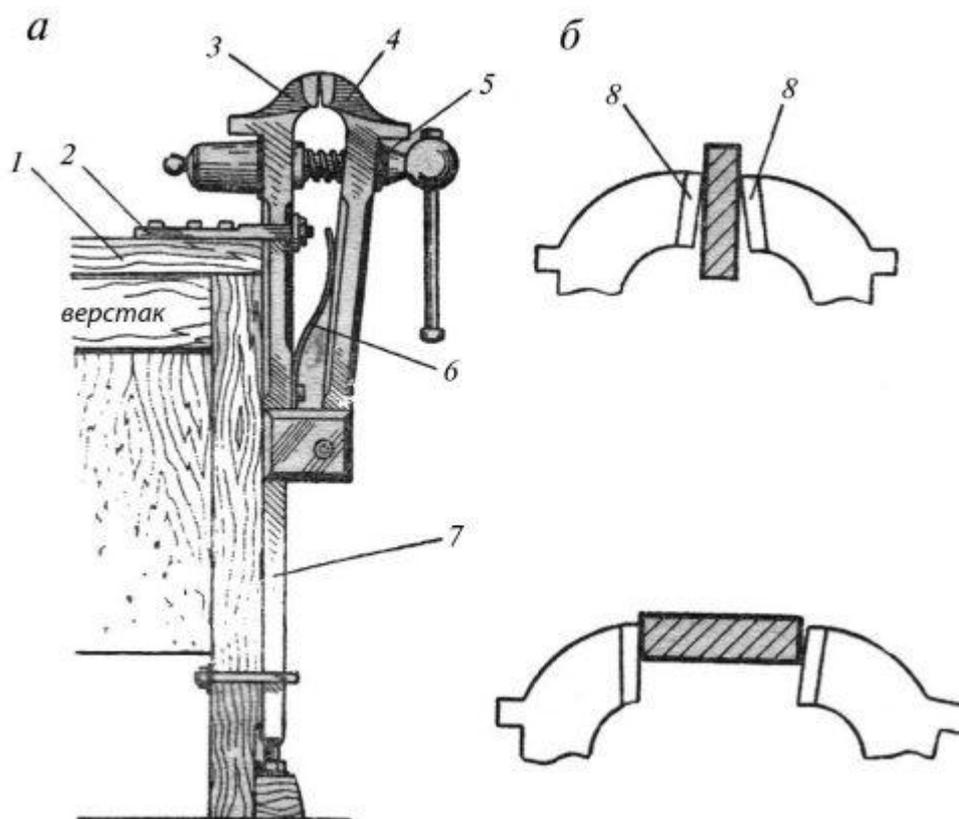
Стуловые тиски: а – общий вид, б – схемы закрепления заготовок
